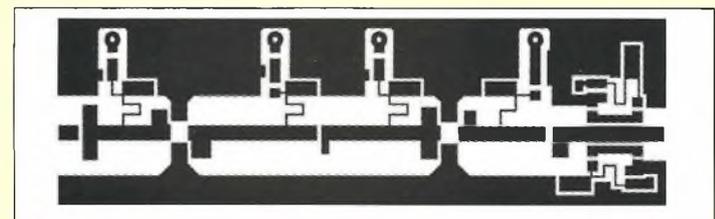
Le dessin du circuit imprimé de l'amplificateur 200 milliwatts à l'échelle 1. Vérifiez la longueur qui doit faire 80 millimètres ainsi que les pistes qui font 2 millimètres de large. Notez par ailleurs que l'emplacement du deuxième transistor est plus petit.
